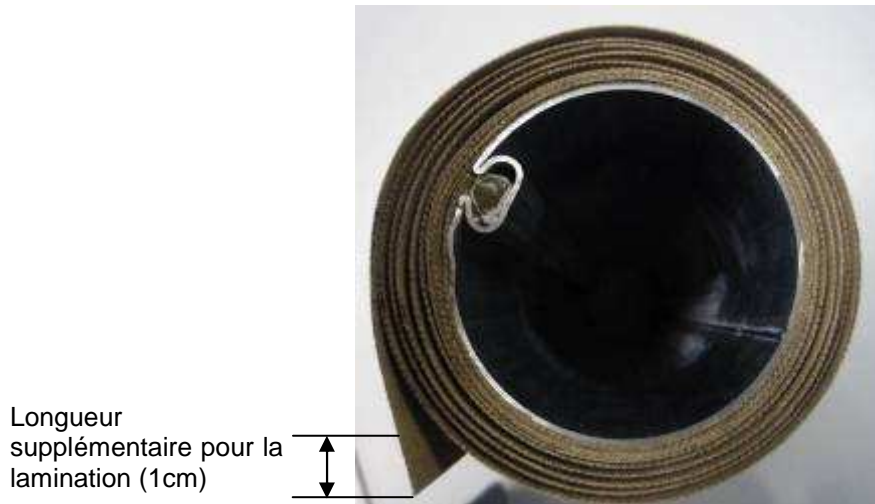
Photographie de l'enroulement d'une toile de store autour d'un tube d'enroulement (vue en coupe sectionnelle)
